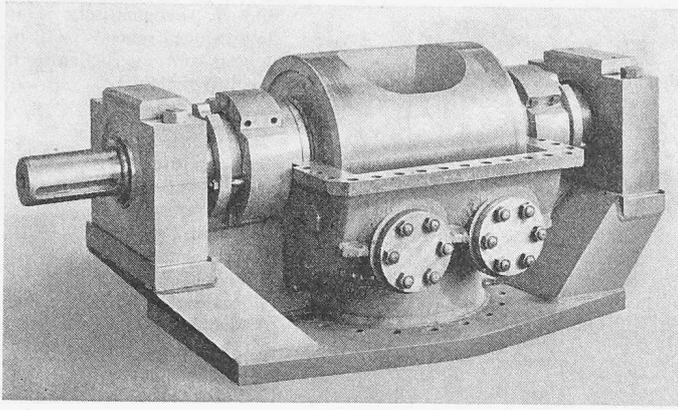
Escher Wyss-Drehventil (Typ DV 500 Z-25) zum Eintrag der getränkten Schnitzel in den unter Druck stehenden Kocher. Die obere Gehäusehälfte mit Verschleissbüchse ist entfernt. Das Bild zeigt Lagerbock und Rotor mit Stopfbüchsen zum Abdichten der Wellenenden.
